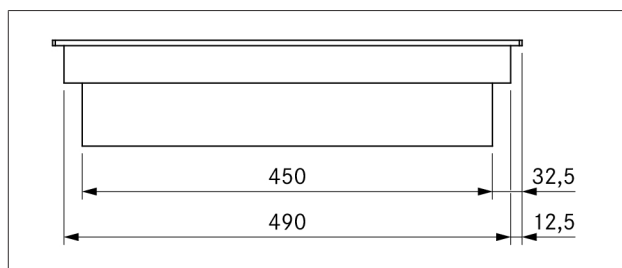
CKIW apparatets dimensjoner sett fra siden
